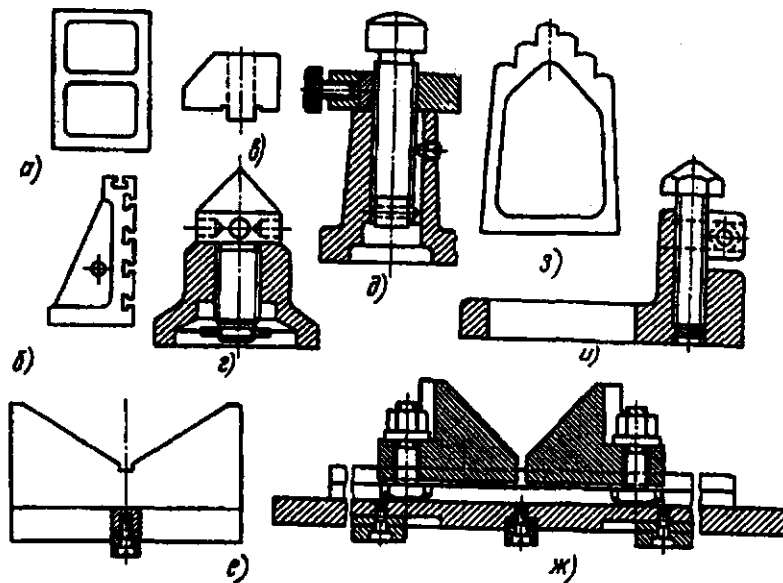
Принадлежности для установки заготовок на расточных станках: а – подкладка чугуная; б – угольник; в – упор; г – домкрат для черных баз; д – домкрат для обработанных баз; е – призма нерегулируемая; ж – призма регулируемая; з – подставка ступенчатая; и – подставка раздвижная
